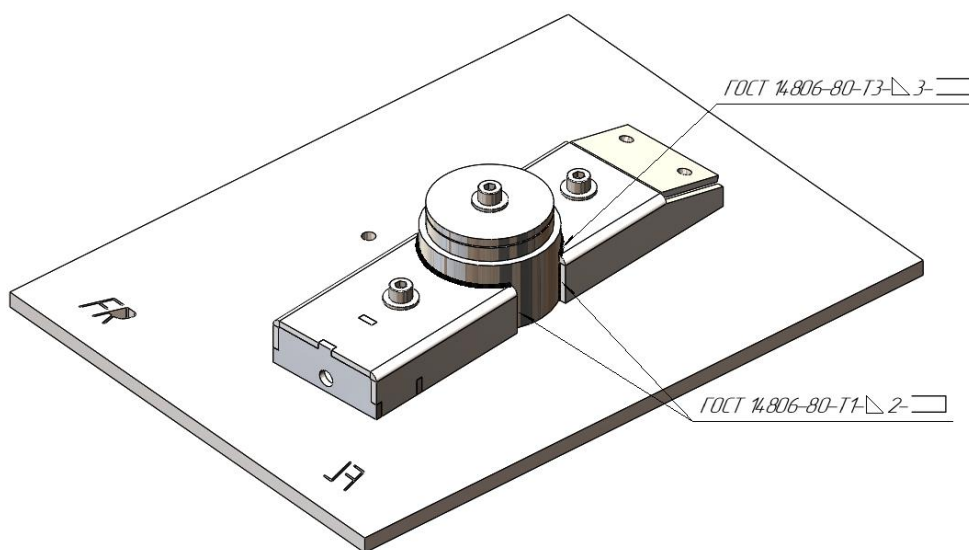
Сварка деталей поворотного кулака
